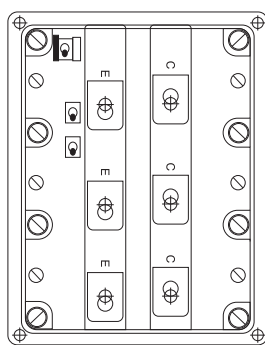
Охладитель с установленным силовым IGBT-модулем с размерами корпуса 170×130 мм
